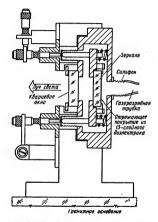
Устройство юстировочного приспособления головки газового генератора.
